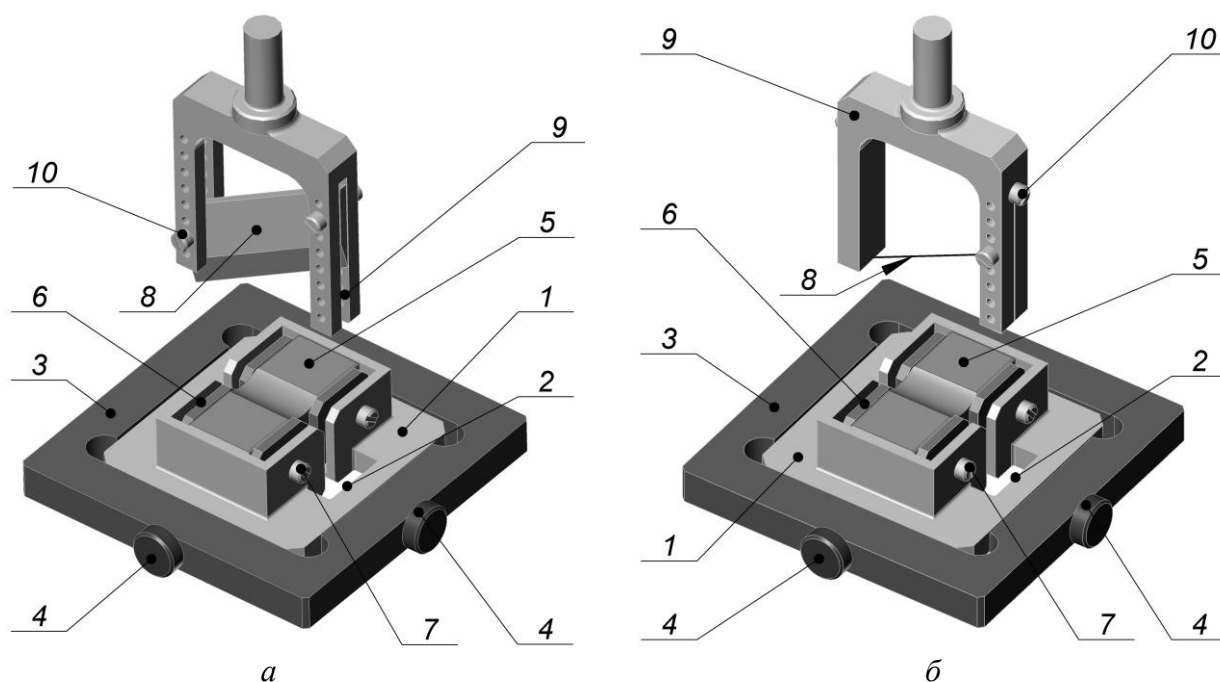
Схемы расположения режущих органов и кассет с образцами материала
